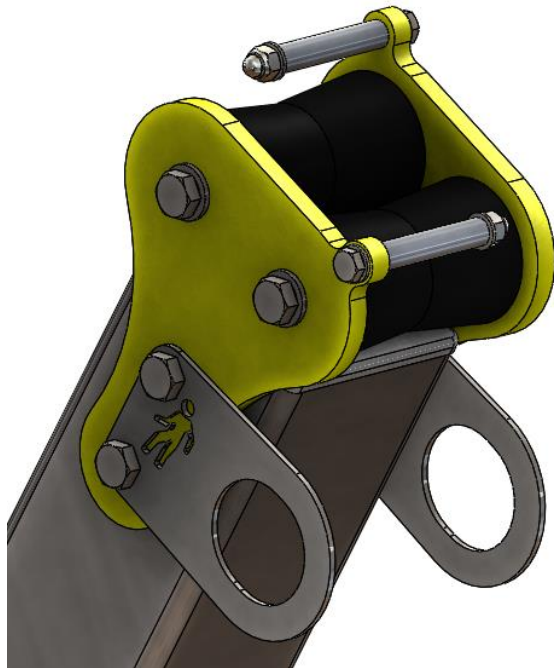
Führung des Arbeitsseils der am Ausleger befestigten Vorrichtung durch die Seilrolle.
